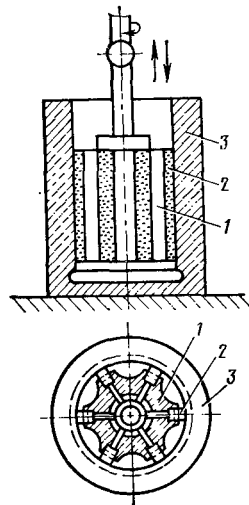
Схема хонингования: 1 - корпус хона; 2 - абразивный брусок; 3 - деталь
